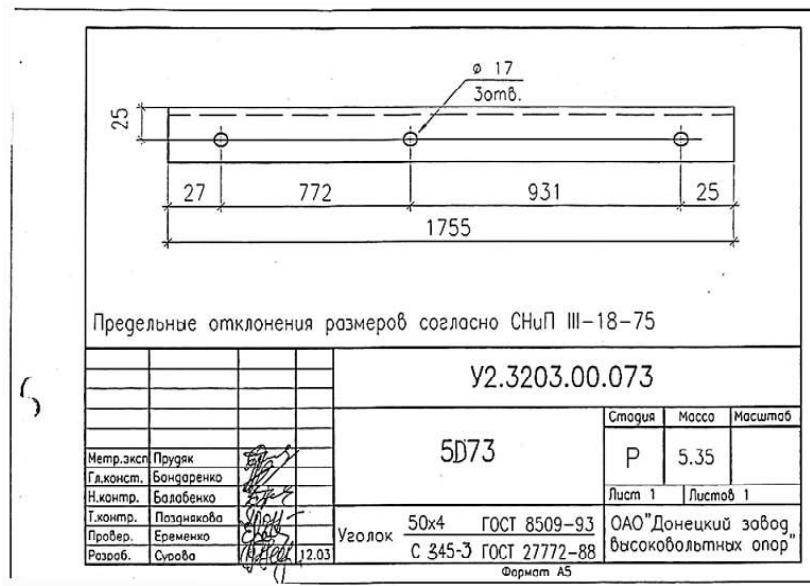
Рабочий чертеж сборочной детали, разработанный в конструкторском отделе ДЗВО.
